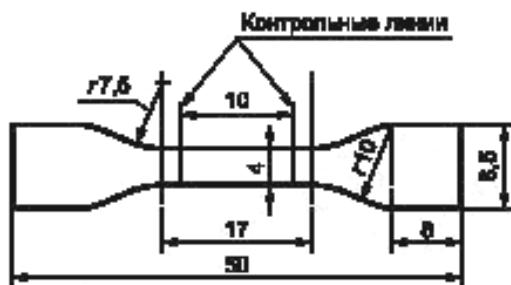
Образец в виде двусторонней лопатки уменьшенного размера
